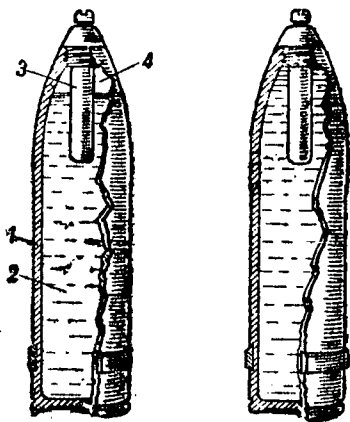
Химический снаряд. Слева — верный чертеж, справа — неверный чертеж. 1 — корпус снаряда; 2 — ОВ; 3 — взрыватель; 4 — воздух и пары ОВ.
